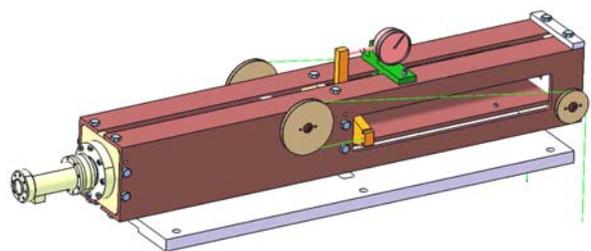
Измерительный стенд для проверки параметров высокоточного линейного привода
